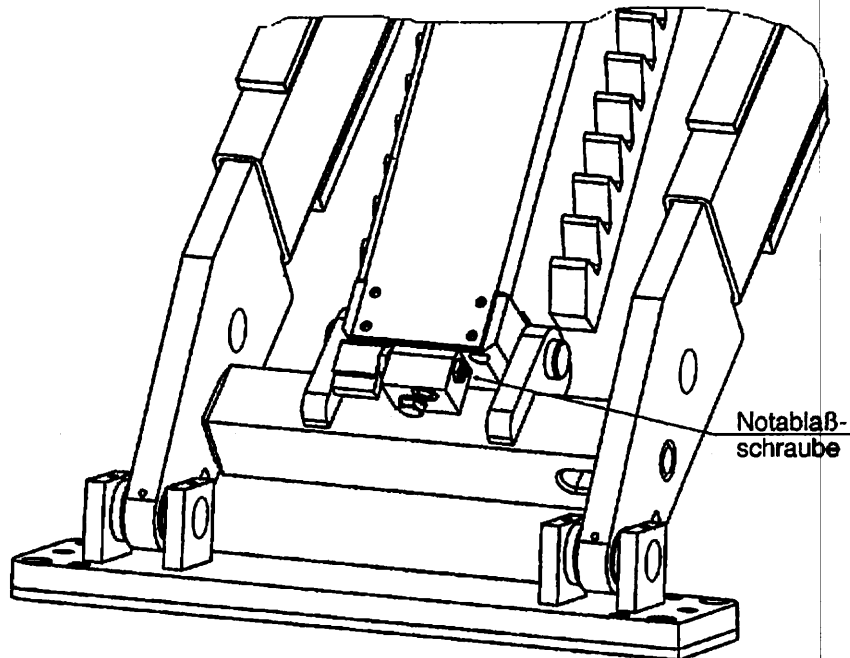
Lage der Notablaßschraube am Sperrblock am Zylinder
